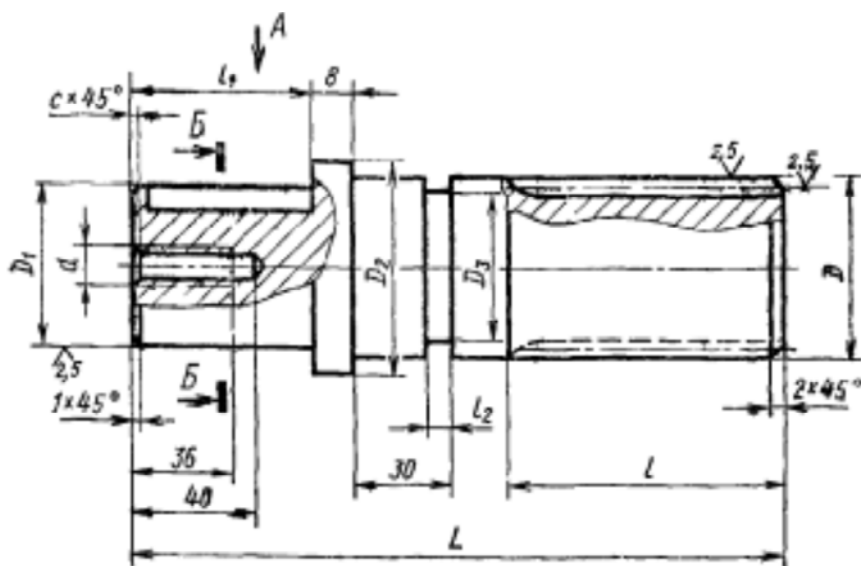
Конструкция и размеры вала-шестерни приспособления для удаления стержней
